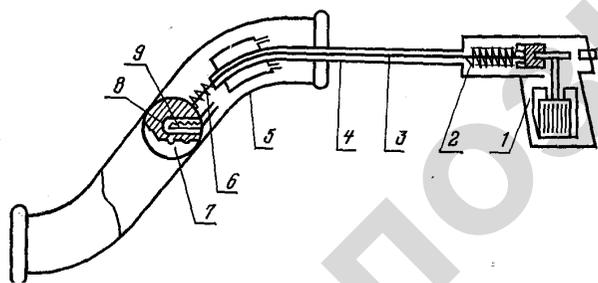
Схема приспособления для калибровки и правки трубопроводов:
